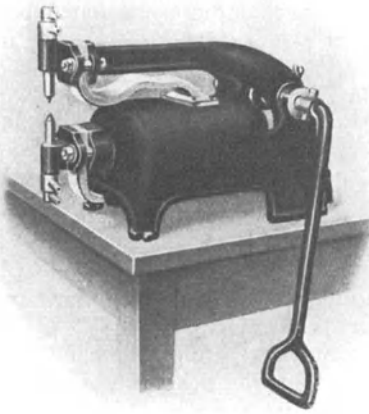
Tisch-Punktschweißmaschine.
